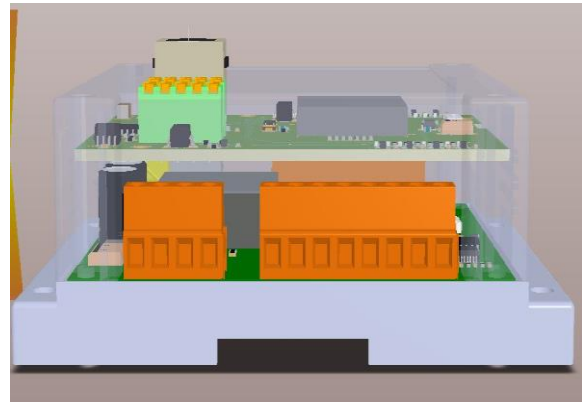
Imagem 3D do PCB inferior e Superior mais caixa
